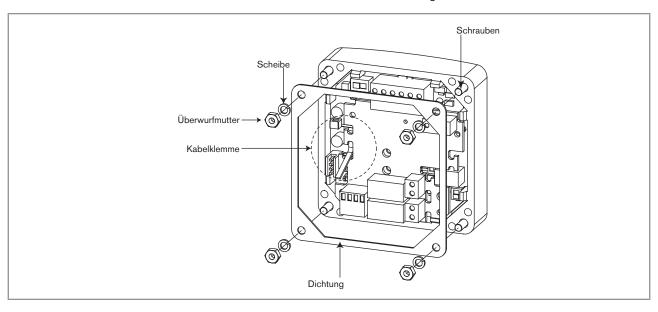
Installation des 8025 in der Schaltschrank-Ausführung
